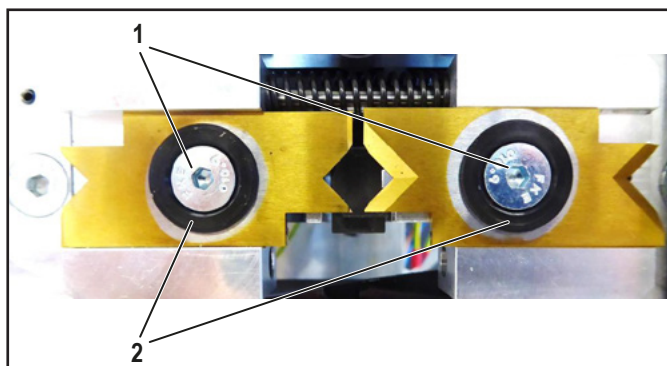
Avisoleringsknivar för Power Stripper 6.0, Power Stripper 16
